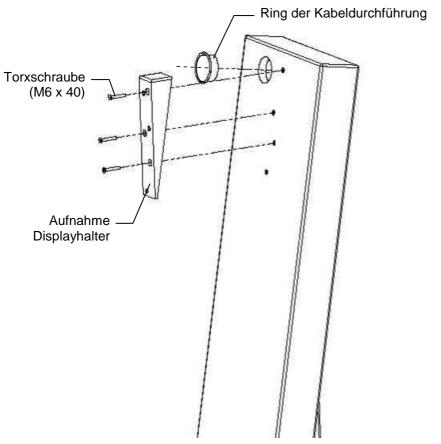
Standfuss - Detailansicht an vorn; Displayhalter und Ring der Kabeldurchführung montieren
